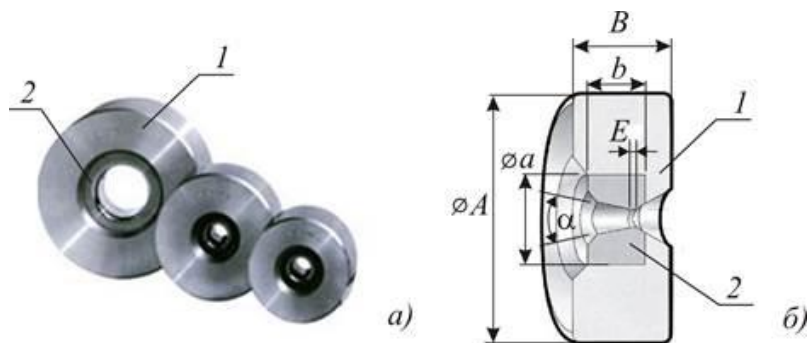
Інструмент для волочіння: а) зовнішній вид волоки, б) геометрія волоки: 1 – стальна волока, 2 – фільтр із твердого сплаву
